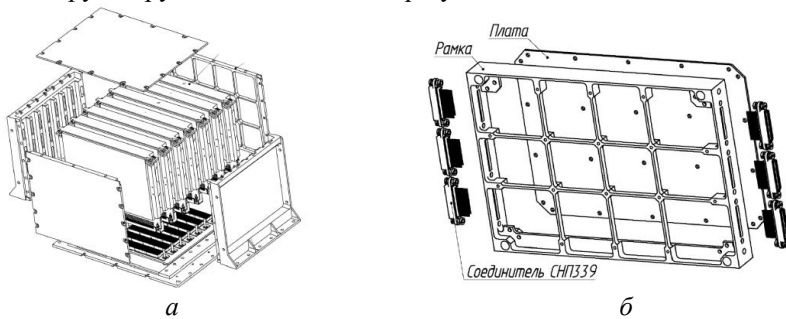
Типовой блок БА: а – общий вид конструкции; б – общий вид несущего модуля
